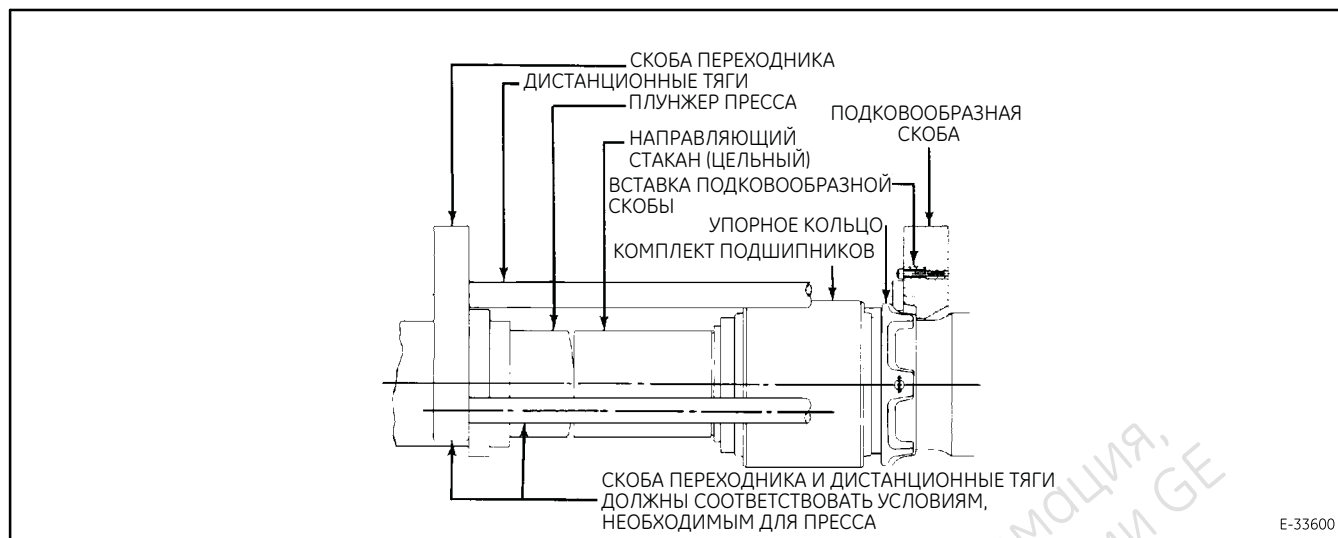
Приспособление для распрессовки подшипника с помощью пресса для распрессовки и запрессовки подшипников или колес.
